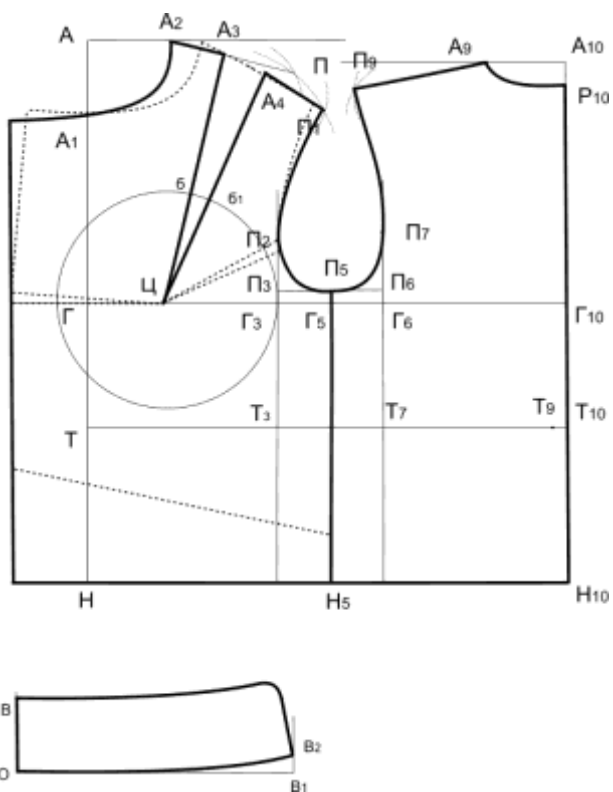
Кресленик базової конструкції та моделювання куртки жіночої
